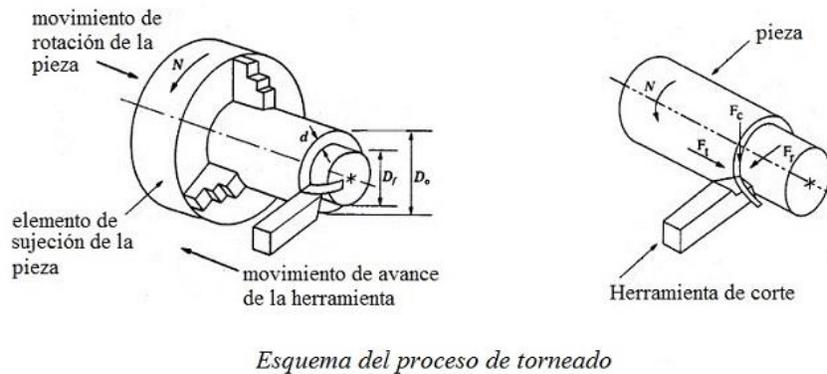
Operación del torneado Fuente. Ingemecánica, 2020
